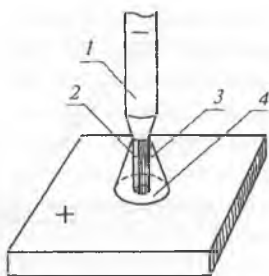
Схема дугового разряда при сварке: 1 — катод; 2 — столб дугового разряда; 3 — пламя сварочной дуги; 4 — анод
